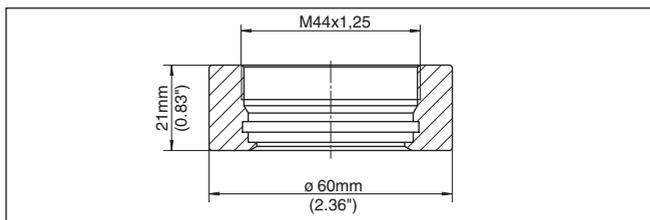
Medidas luva para soldagem M44 x 1,5 - VEGABAR 82, 83
